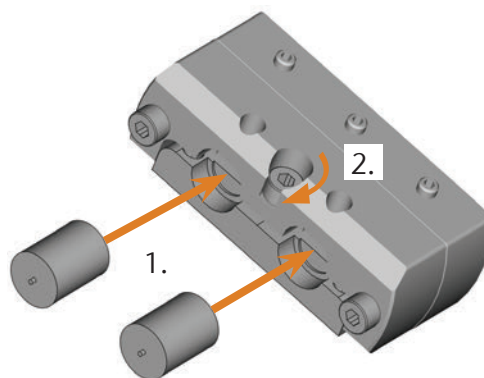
FIJACIÓN DE LOS PILARES PREFACE®
